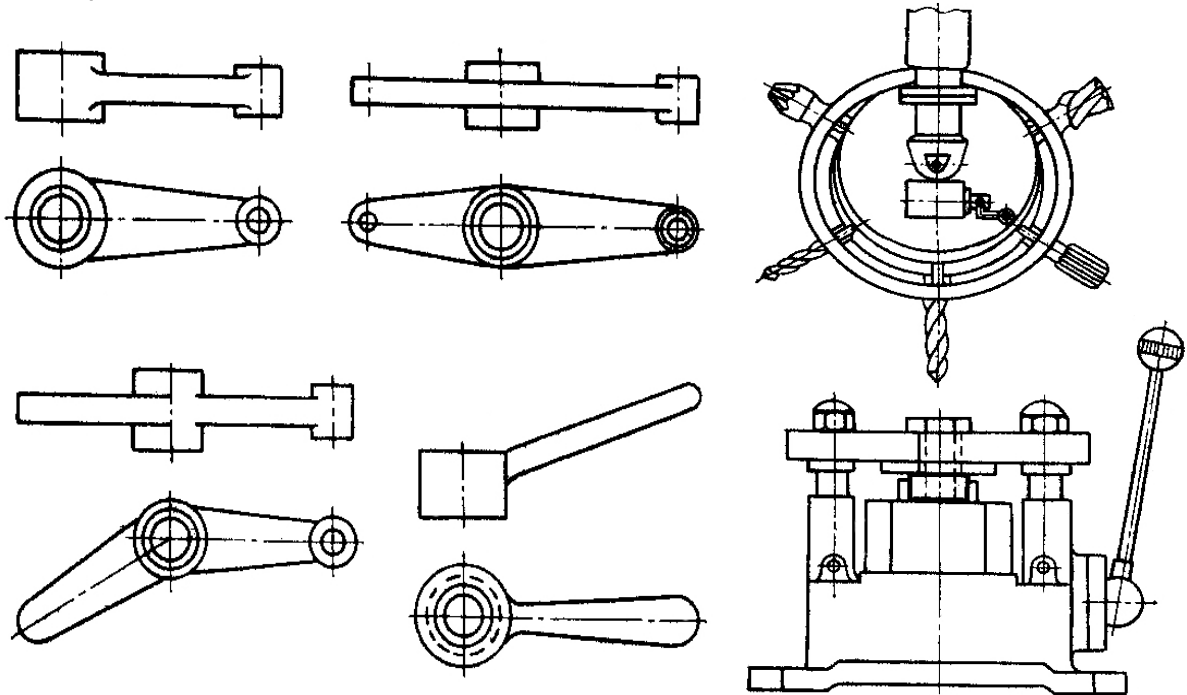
Група деталей і групове оснащення свердлильного верстата
